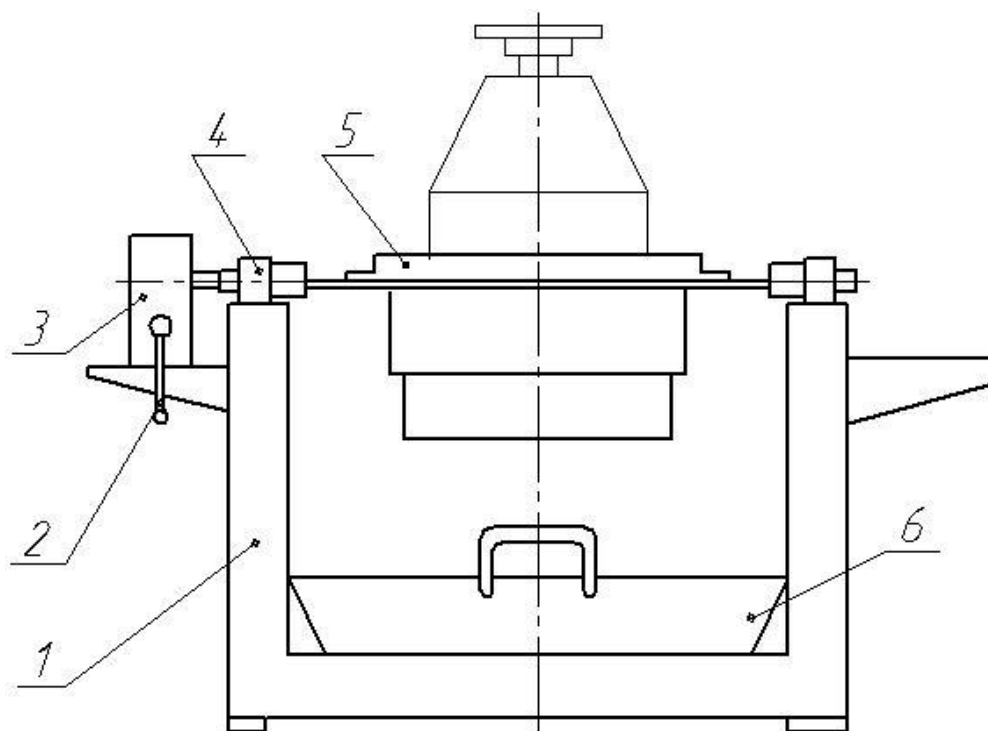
Схема стенда для разборки и сборки редуктора заднего моста автомобиля БелАЗ, модель 24-15 концерн ПСК (Санкт-Петербург)
